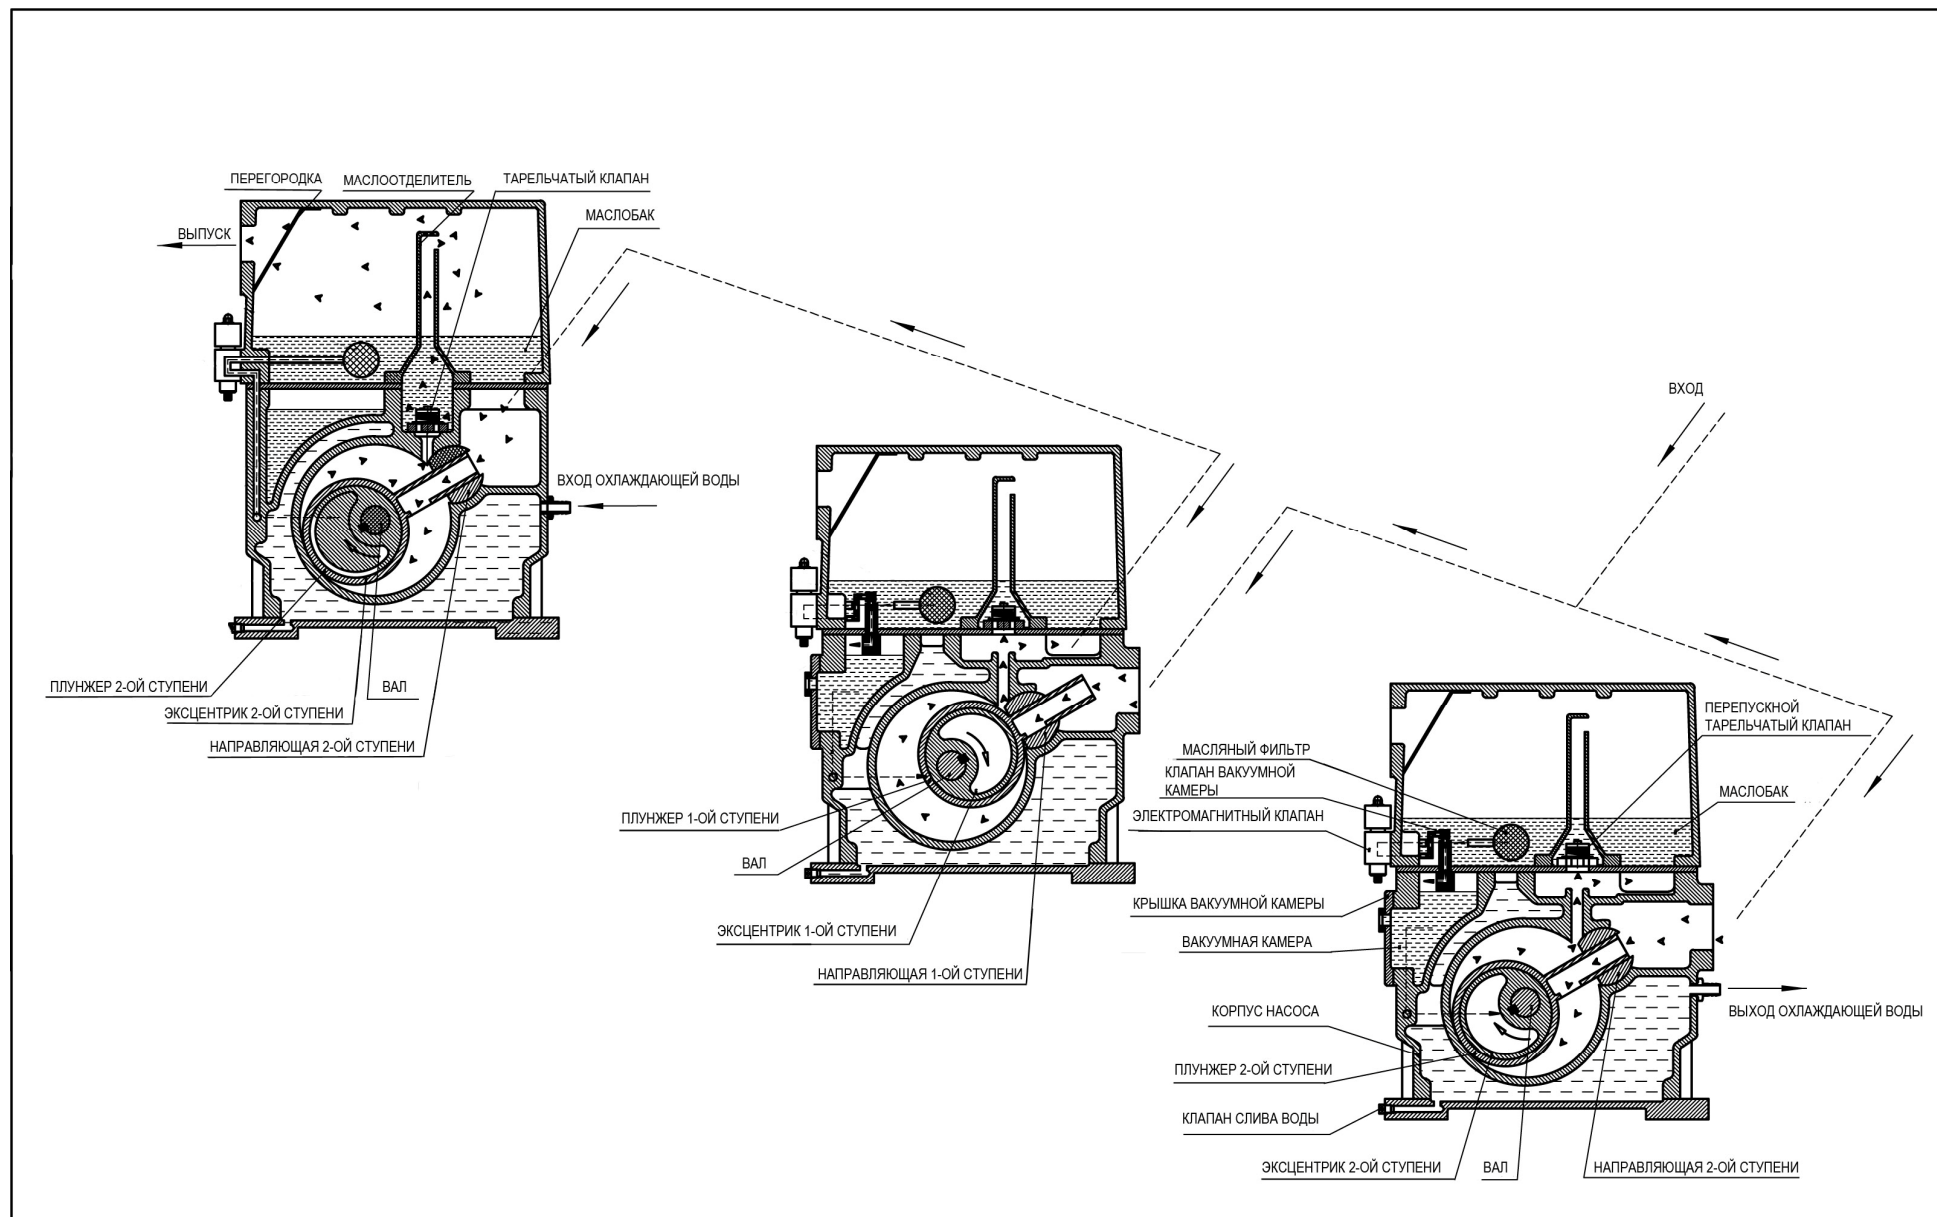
Двухступенчатый трехплунжерный агрегат. Схема работы
